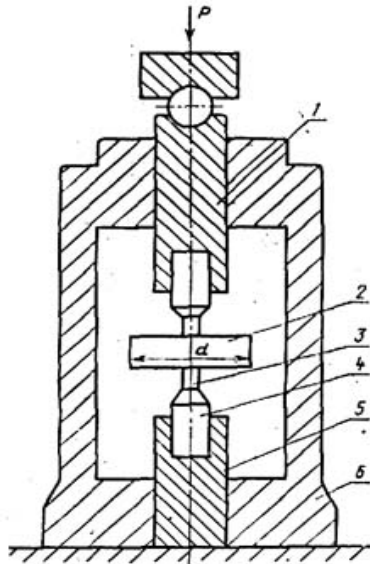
Схема установки для испытания образцов с помощью соосных пуансонов: 1 – верхний шток; 2 – образец; 3 – пуансон; 4 – вкладыш; 5 – нижний шток; 6 – корпус.
